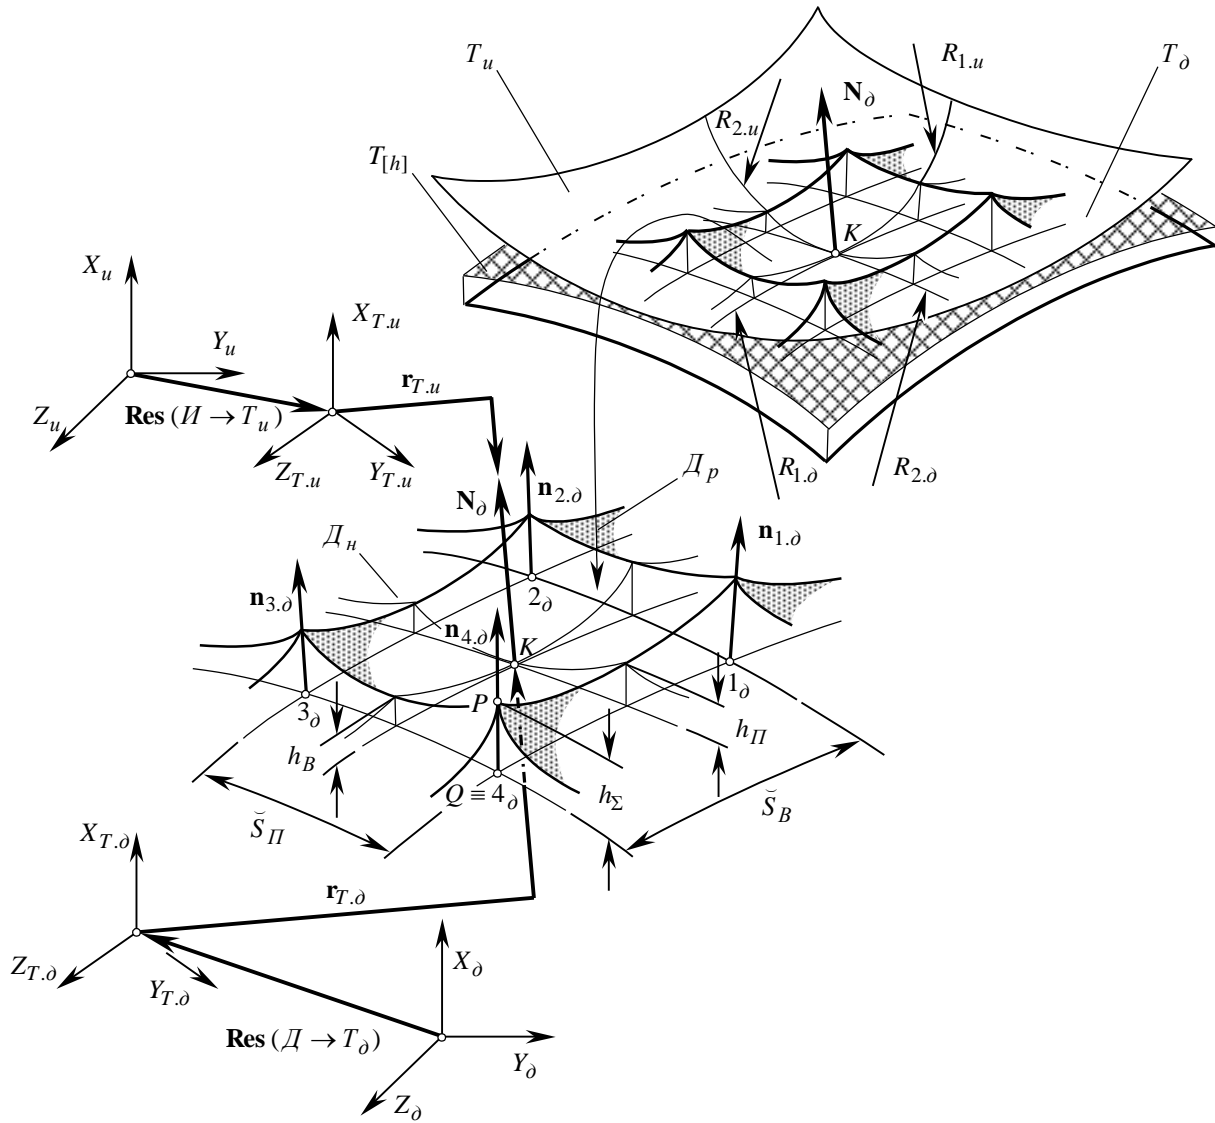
Элементарная ячейка на формообразованной поверхности  $D$  детали.
